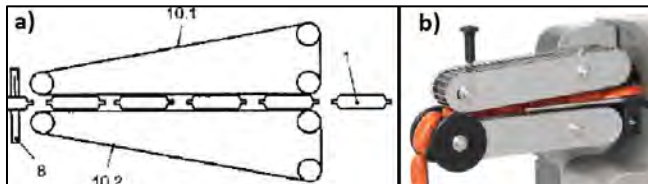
a) *Conveyor gripper* (patente DE102004056038A1); b) *Conveyor gripper* comercial.
